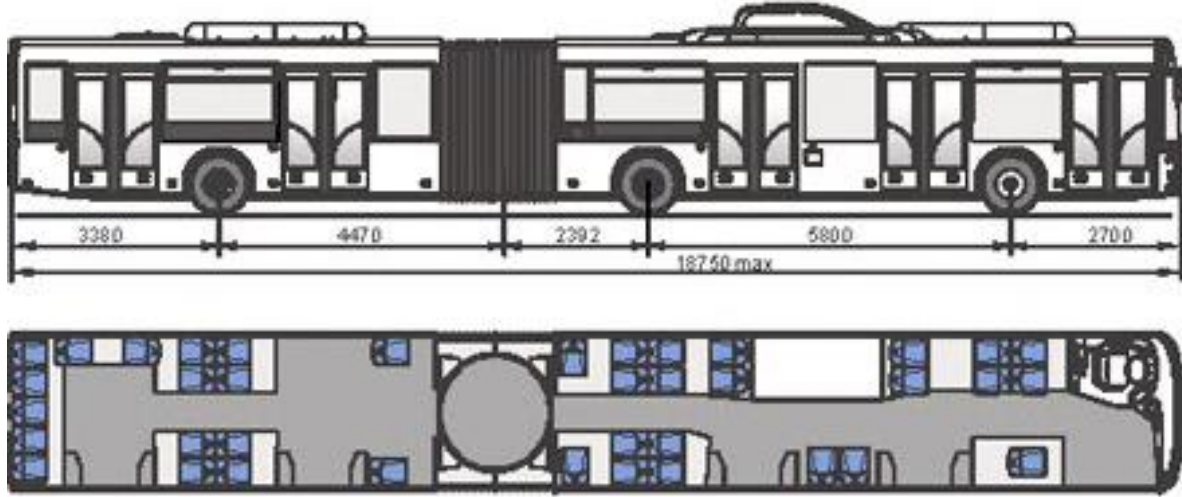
Загальний вигляд шарнірно-зчленованого автобуса
